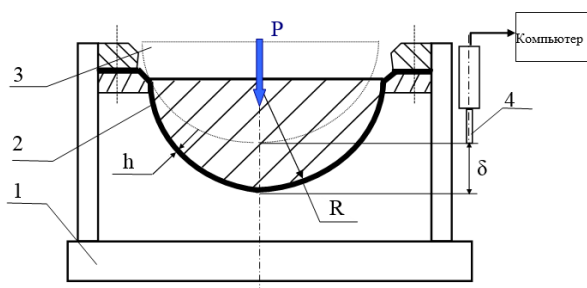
Установка для гибки листовой заготовки по цилиндрическому формблоку:
